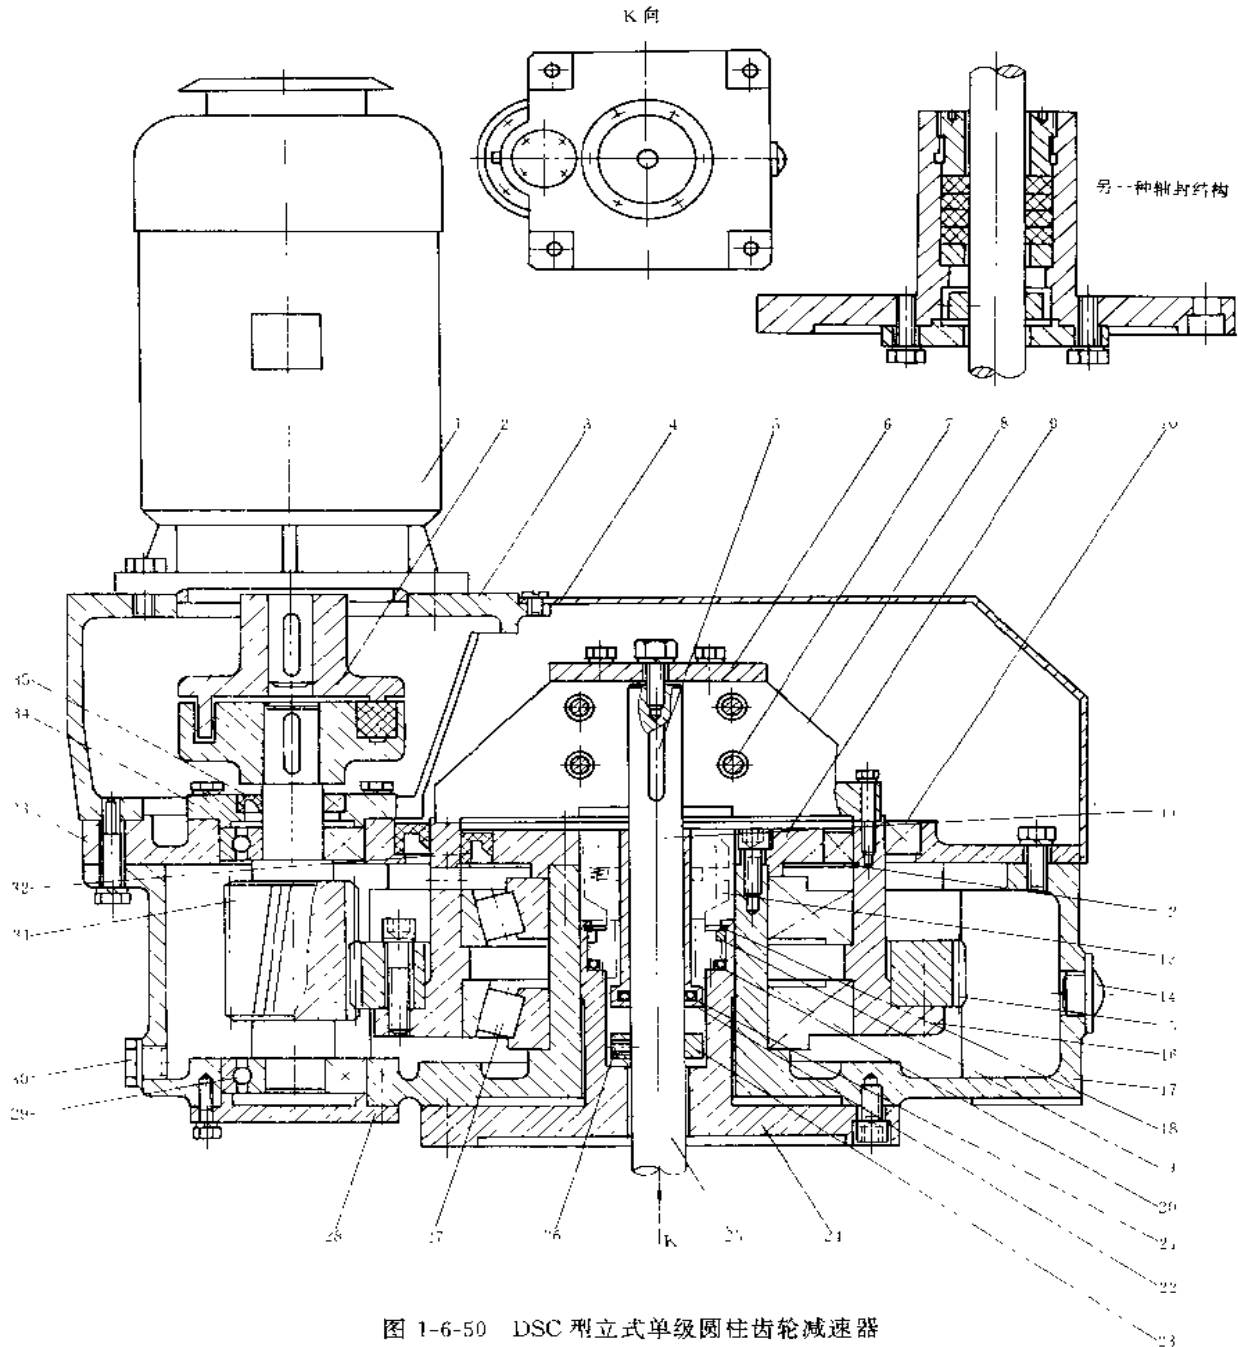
DSC 型立式单级圆柱齿轮减速器
